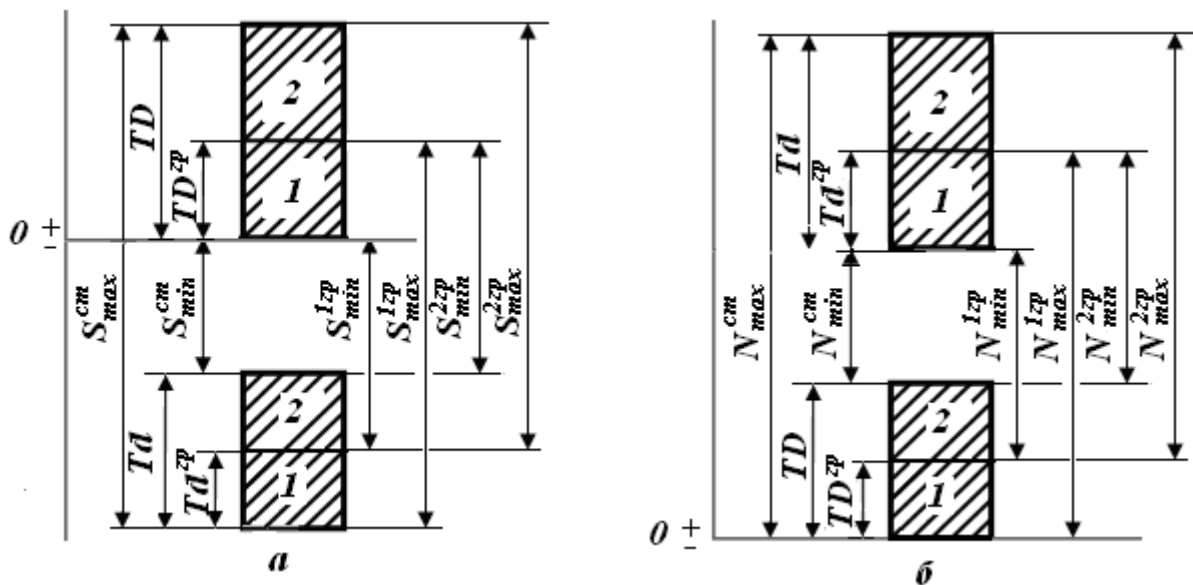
Схеми розташування полів допусків для посадок із зазором (а) і з натягом (б)
